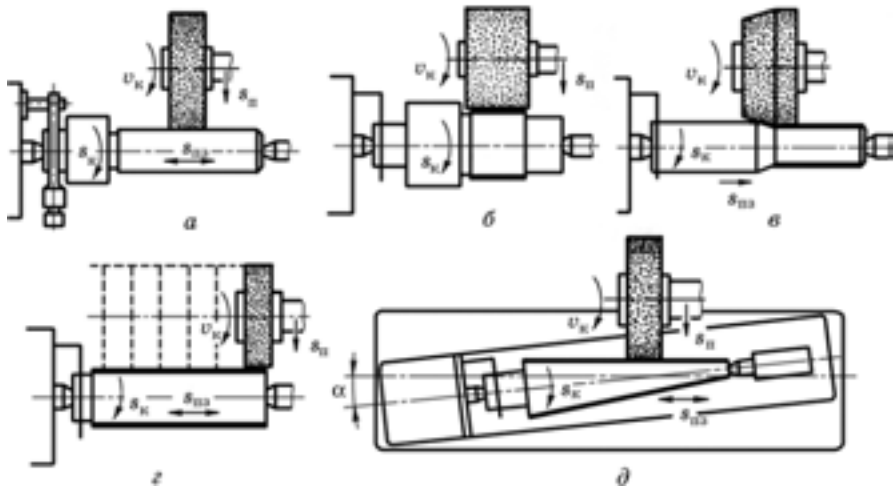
Схеми оброблення заготовок на круглошліфувальних верстатах
